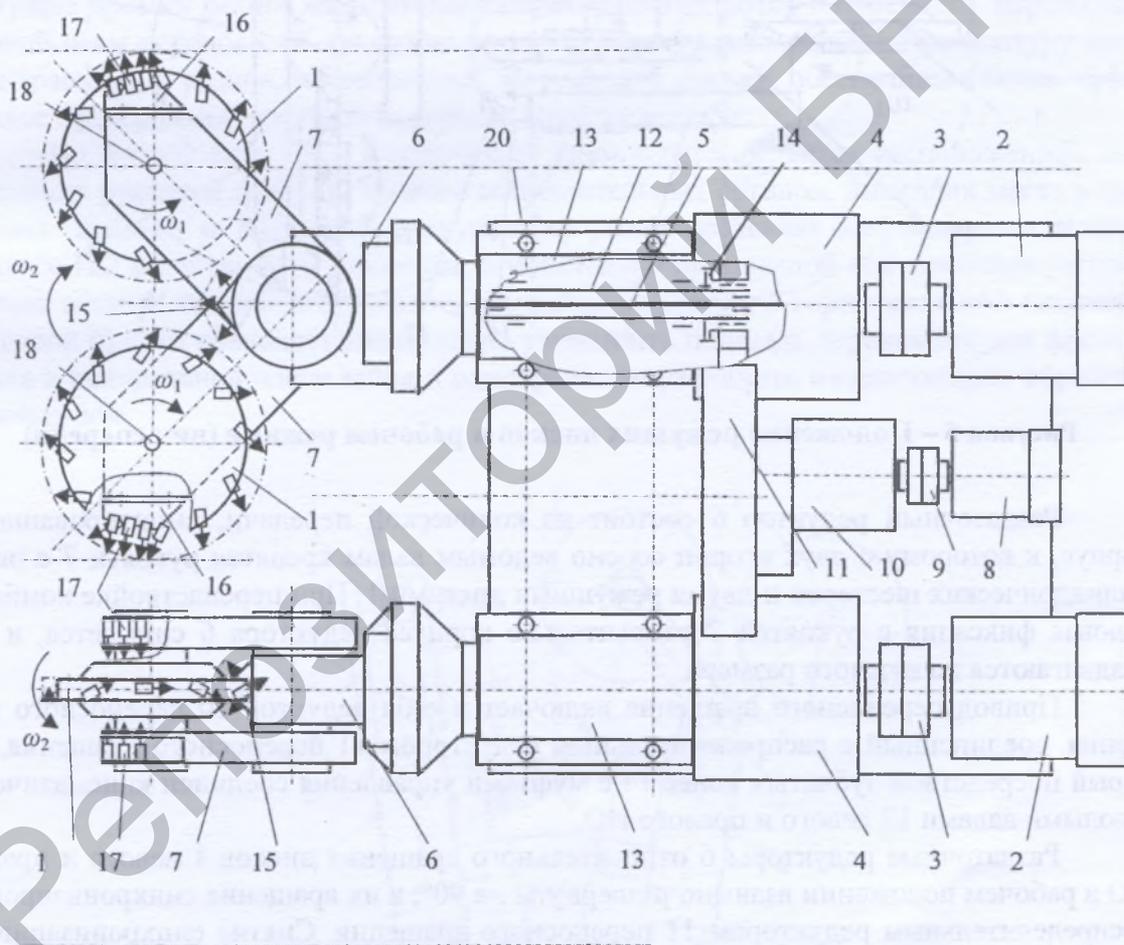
Планетарный сдвоенный исполнительный орган проходческо-очистного комбайна (вид сверху)
